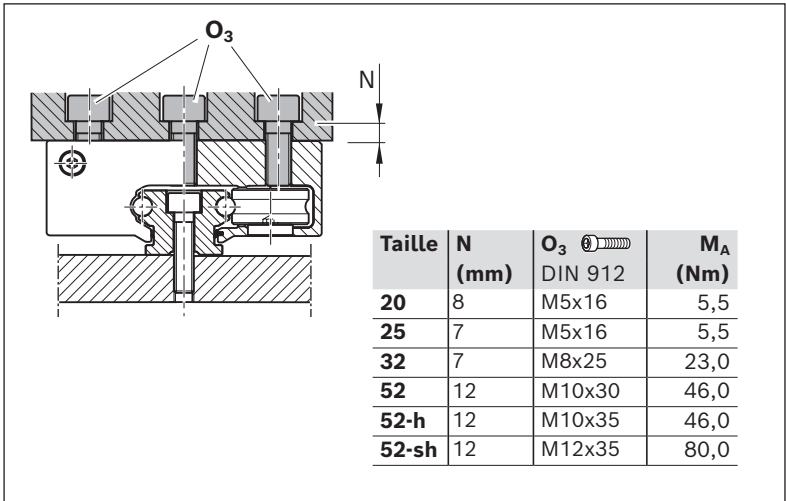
Montage de l'élément périphérique sur le guide standard et le guide Super
